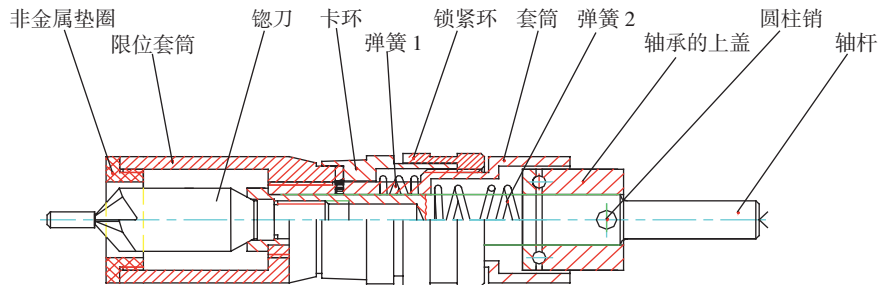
可换铤刀头及刀杆尾柄处安装轴承结构
